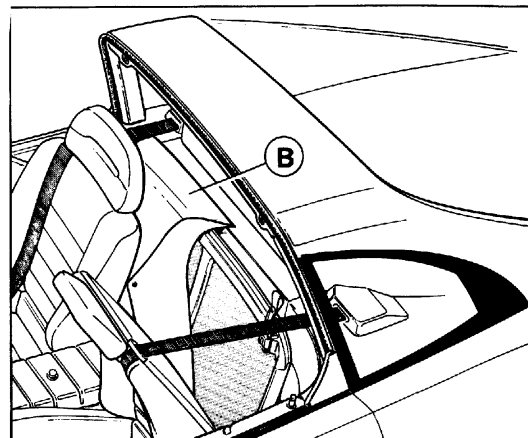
26 - 27 - Capot (démontage et montage)
